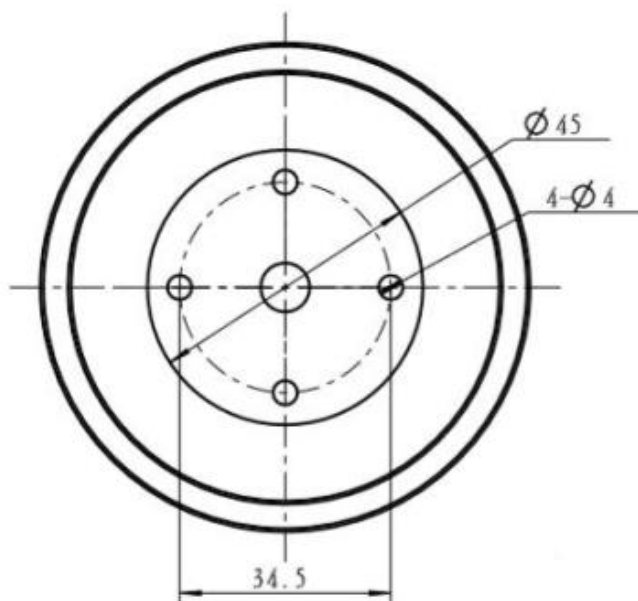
Размеры датчика шума (внешнего) ICB300-06
